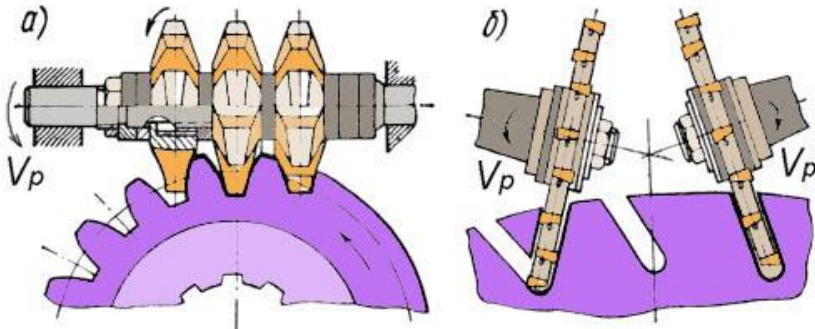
Нарізання зубів дисковими модульними фрезами
